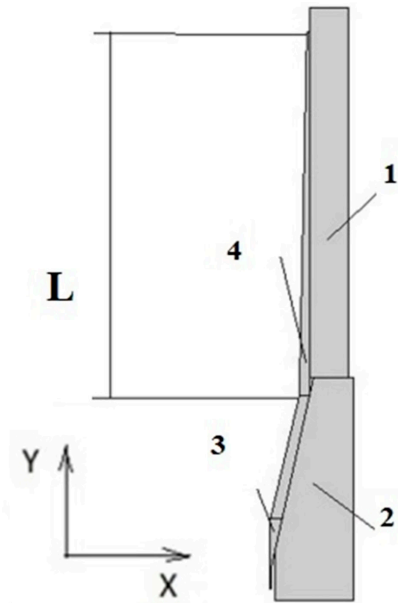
Схема зоны прохождения корочки заготовки: 1 – медная стенка; 2 – подвижный агрегат; 3 – очаг деформации; 4 – корочка; L – пояс формирования корочки заготовки
